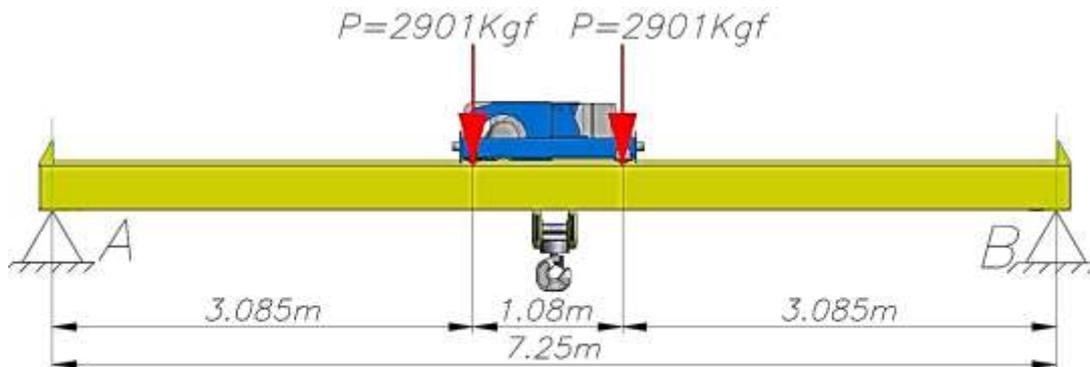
Esquema viga puente Fuente: (Autor)
